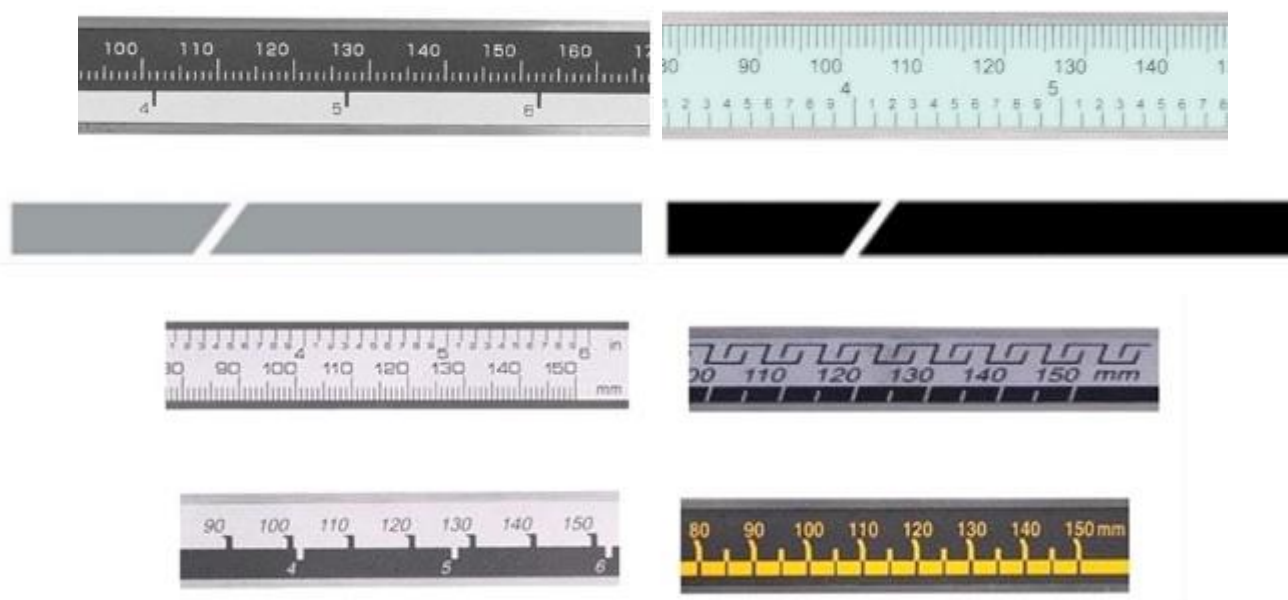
Общий вид шкал на штанге штангенциркуля
